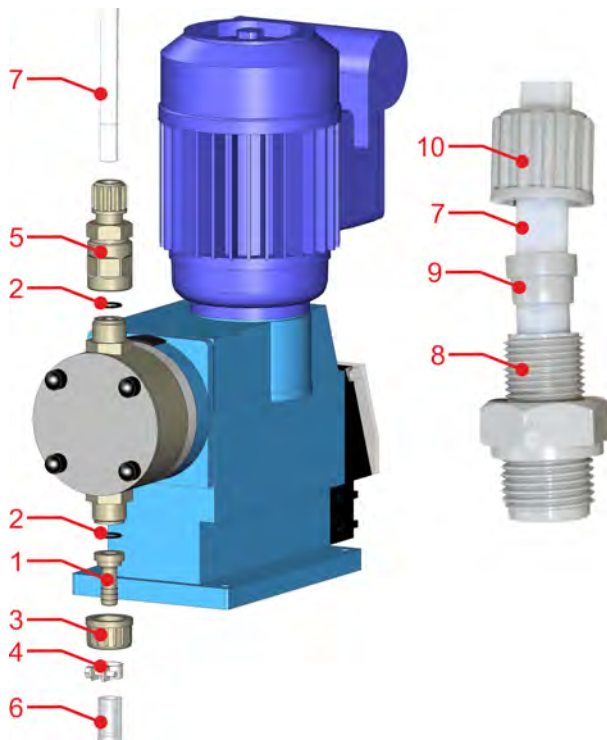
Montage Pumpenanschlusset EMP III Pumpe (54 l/h)
